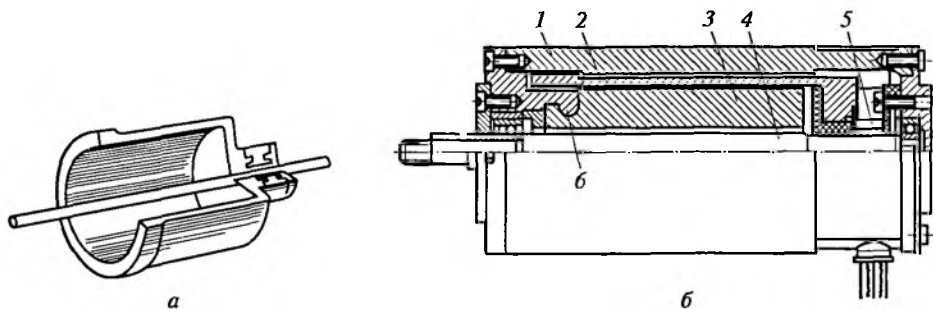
Полый немагнитный якорь (*а*) и устройство исполнительного двигателя постоянного тока с полым немагнитным якорем (*б*):
